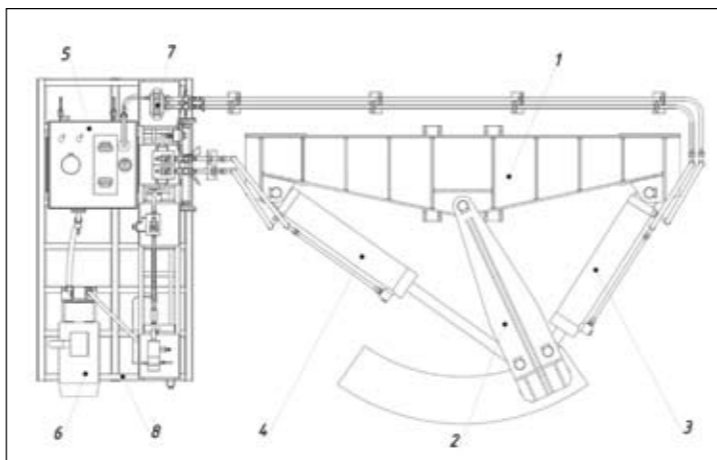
Общий вид экспериментального моделирующего комплекса: 1 – станина; 2 – поворотное водило; 3 – рабочий гидроцилиндр; 4 – нагрузочный гидроцилиндр; 5 – гидробак; 6 – насосный агрегат; 7 – клапанный стол; 8 – рама
